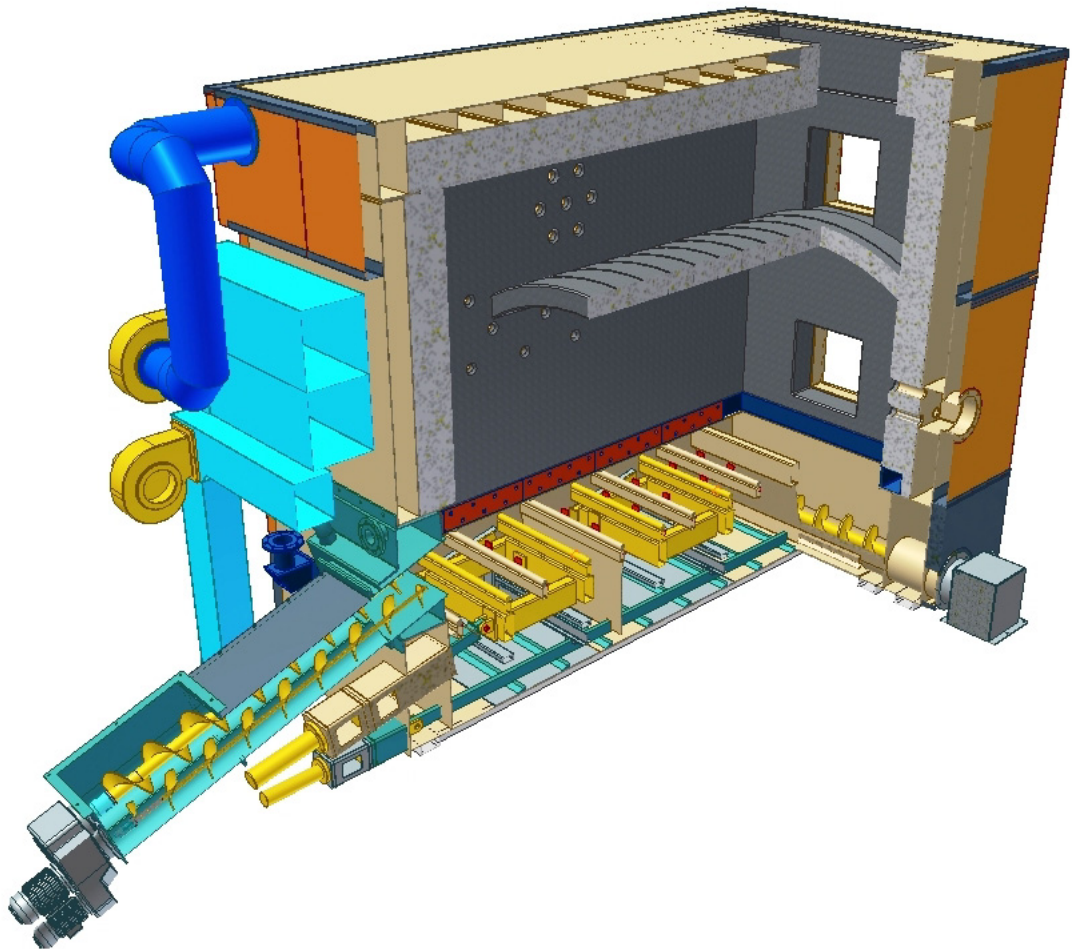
Sezione della camera di combustione a griglia mobile orizzontale
